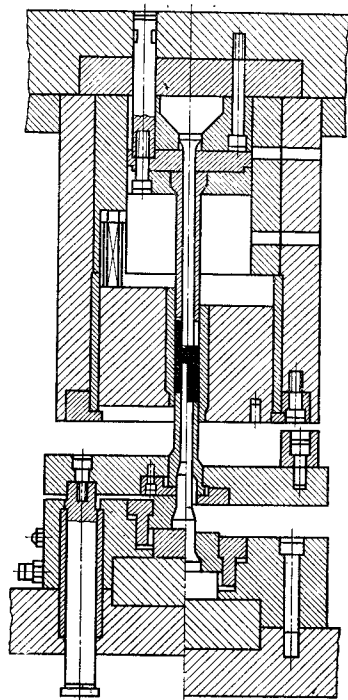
Схема наладки штампа для двухстороннего выдавливания с трубчатым выталкивателем
